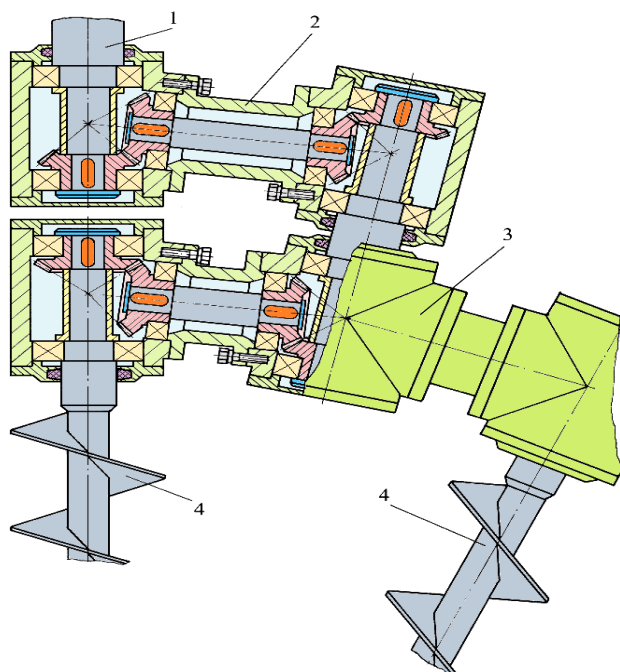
Элементы конструкции привода конического бипланетарного смесителя.
